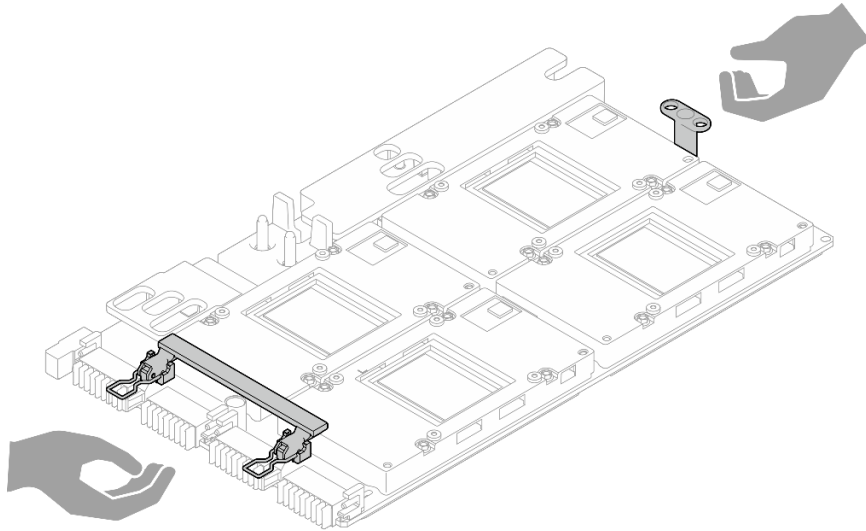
Extracción de la Conjunto de placa de GPU SXM5 de la caja del paquete
